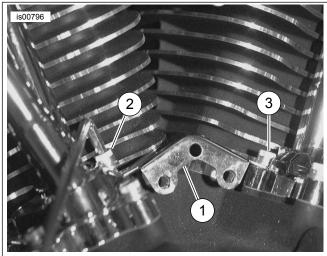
Suporte da tampa do tucho de válvula dianteira instalado
